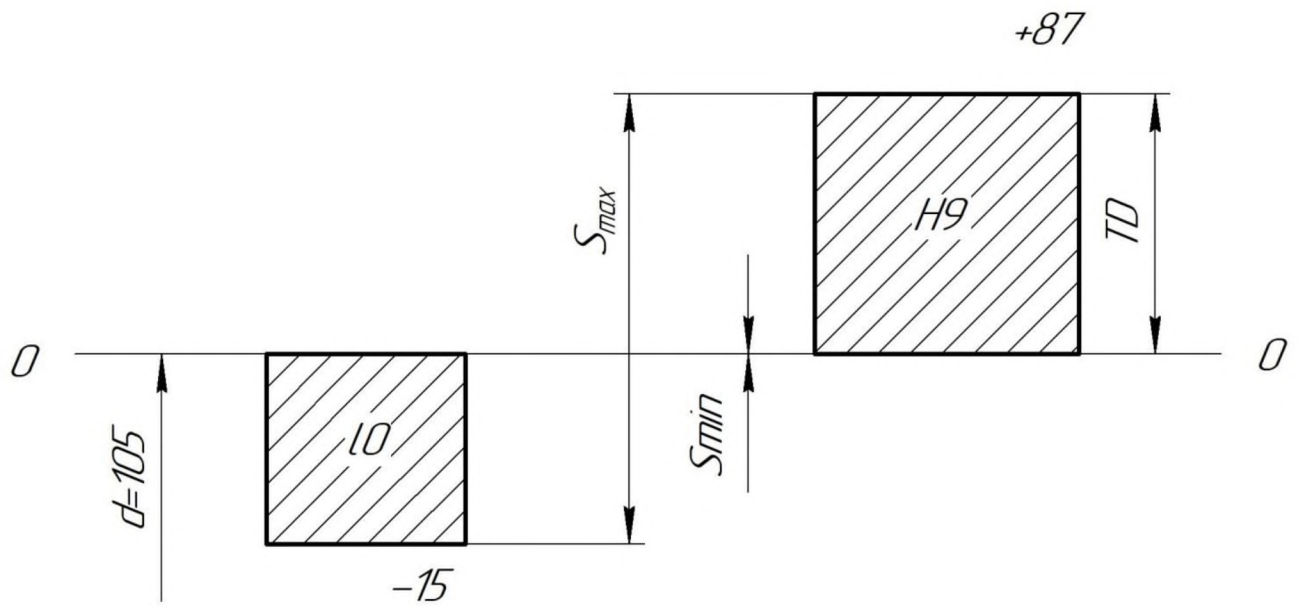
Схема полів допусків з'єднання деталі з підшипником
